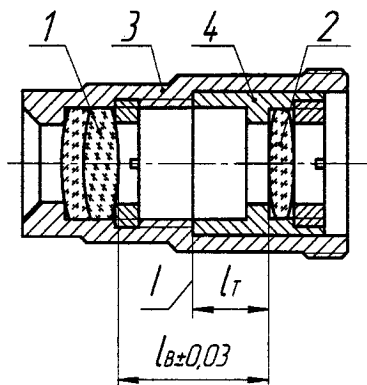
Конструктивна схема об'єктива з підрізуванням базового опорного кільця
